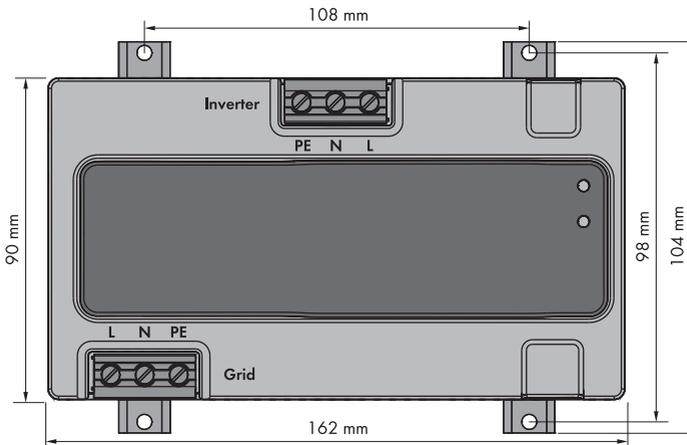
Bemaßung des Sunny Multigate und der Bohrlöcher für Montage mit Schrauben
